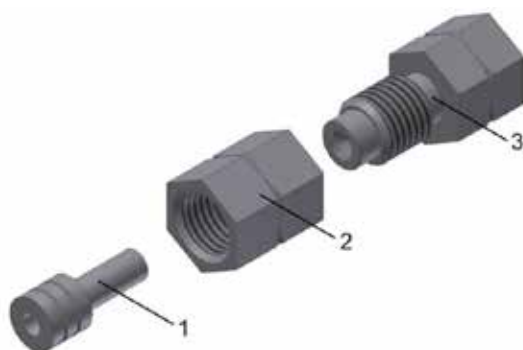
Приспособление для монтажа блочных резьбовых соединителей типа розетка в тракте 2,92/1,27 мм (ЖНКЮ.296371.030-02)
